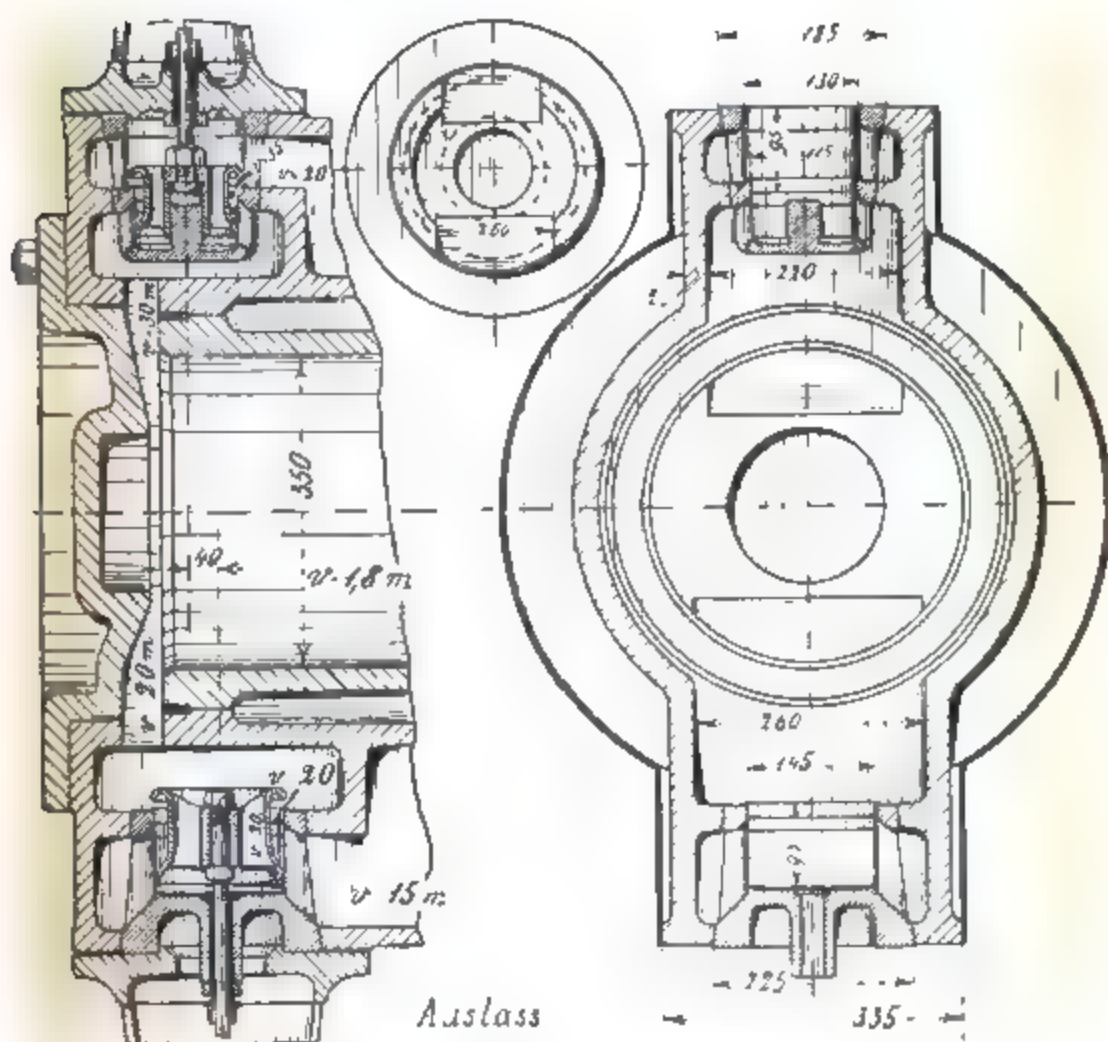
1251. Ventilsteuerung für 350 Cylinderdurchmesser.
